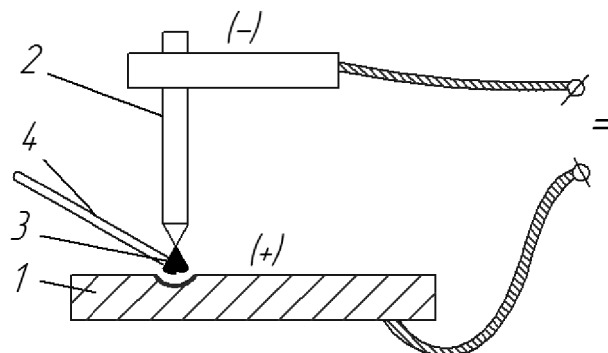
Схема дуговой электросварки по Н.Н. Бенардосу
